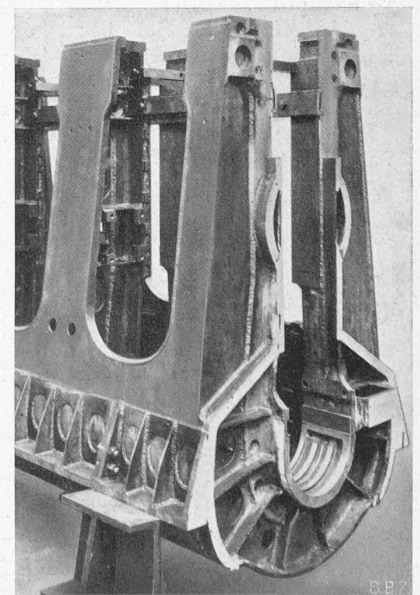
Geschweisster Rahmen zum Motor Abb. 1.
